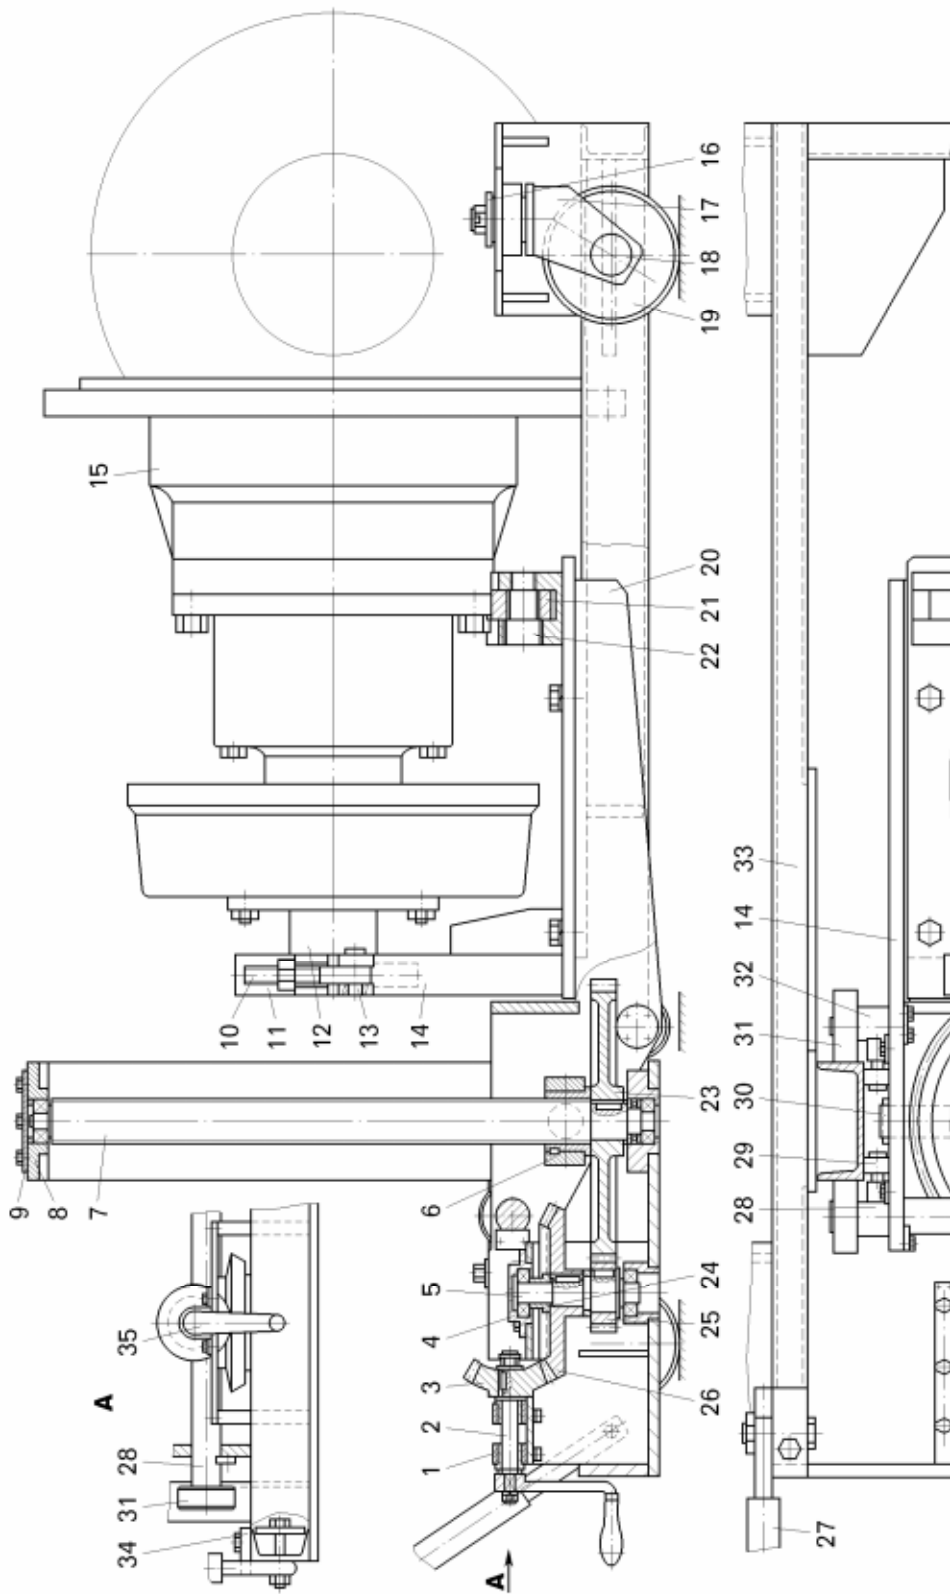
Тележка для демонтажа главной передачи:
